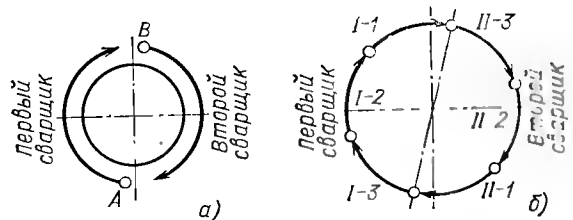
Порядок наложения валиков первого слоя шва горизонтального стыка труб при сварке двумя сварщиками.
